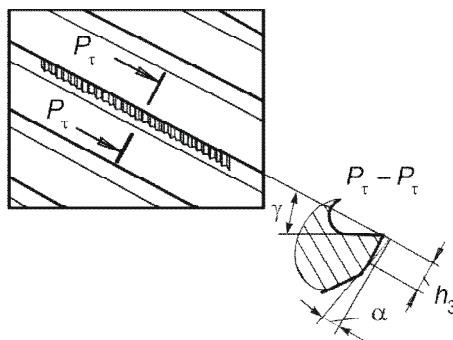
Схема износа осевой (цилиндрической) фрезы
